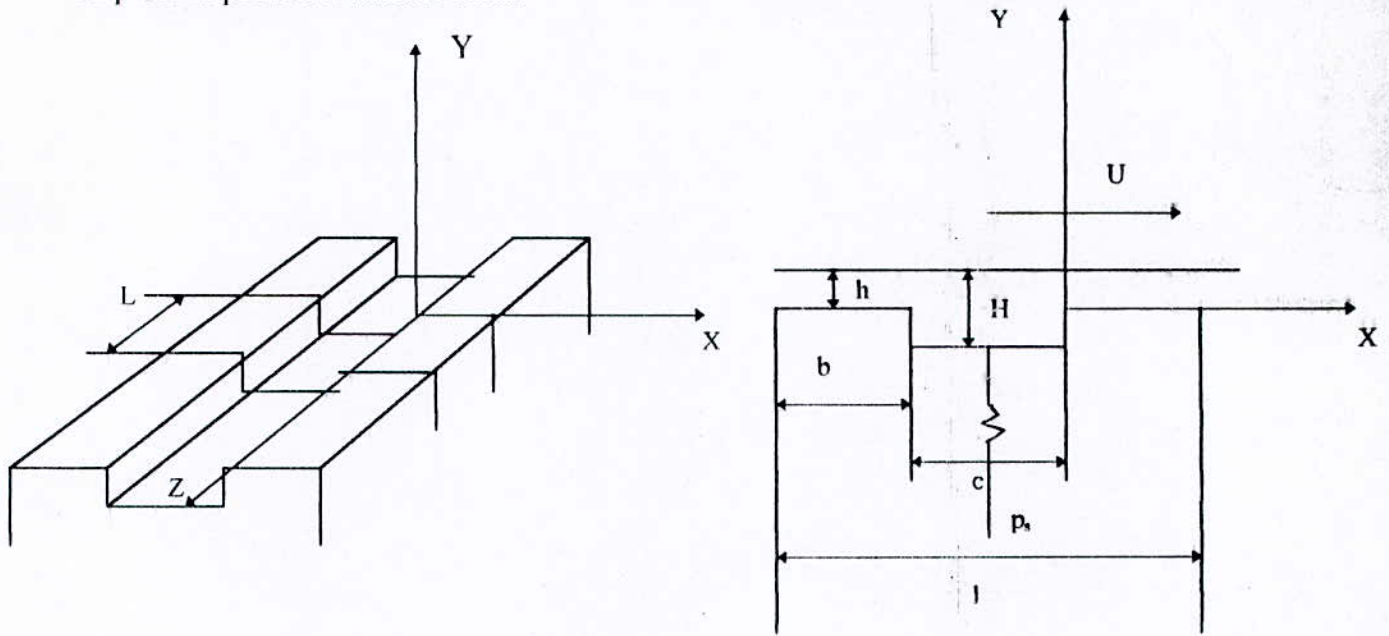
Schématisation d'une butée plane infiniment longue
